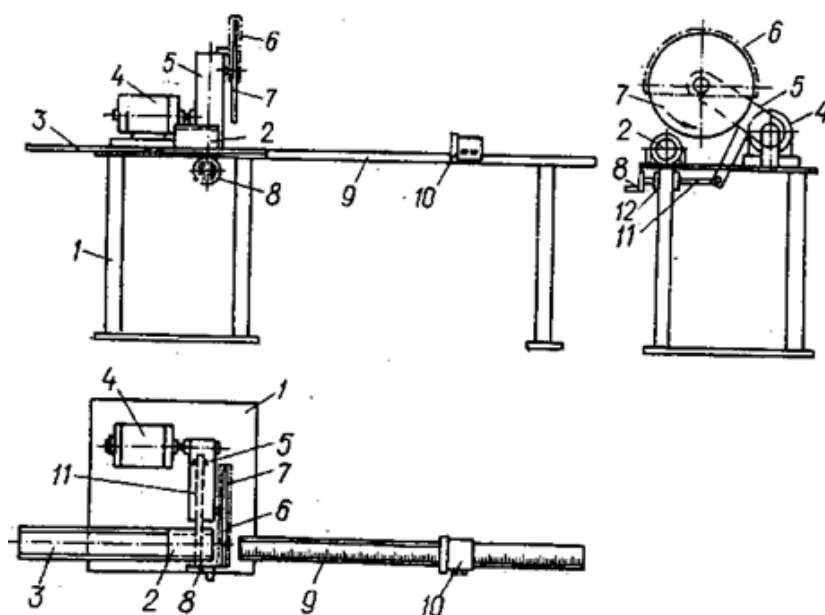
Схема верстату для розмітки і перерізування поліетиленових труб
